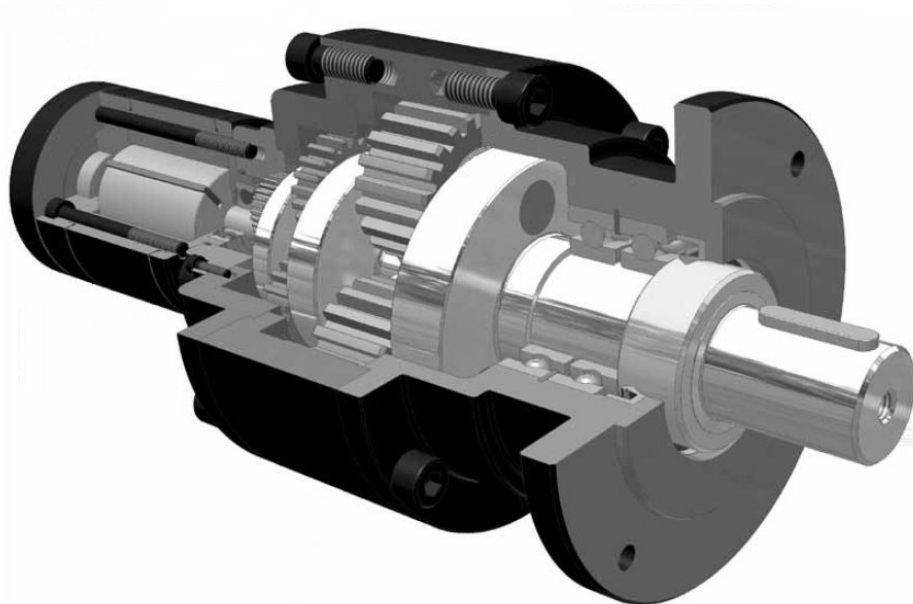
Funkční princip lamelového pneumatického motoru [2]
